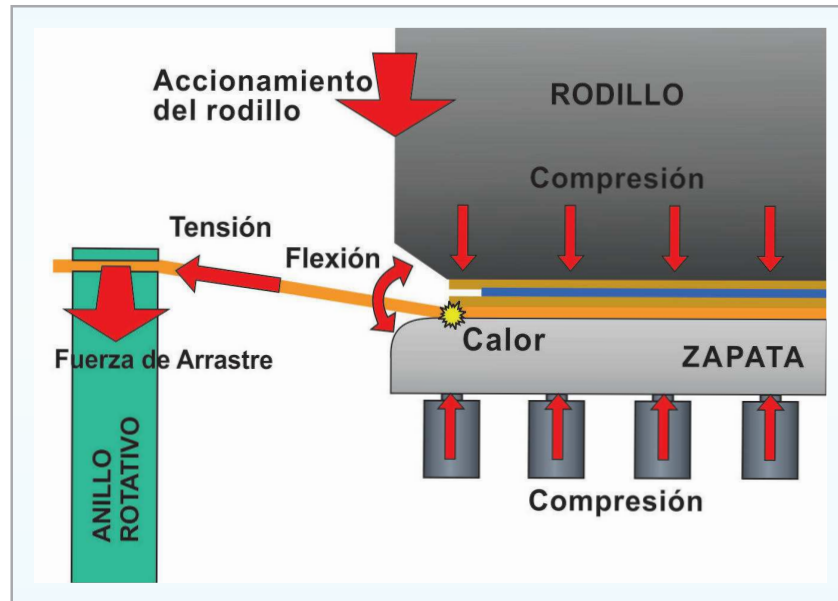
Muchas de las fuerzas bajo las cuales a la manta se la somete están concentradas en el lado de la zapata.
